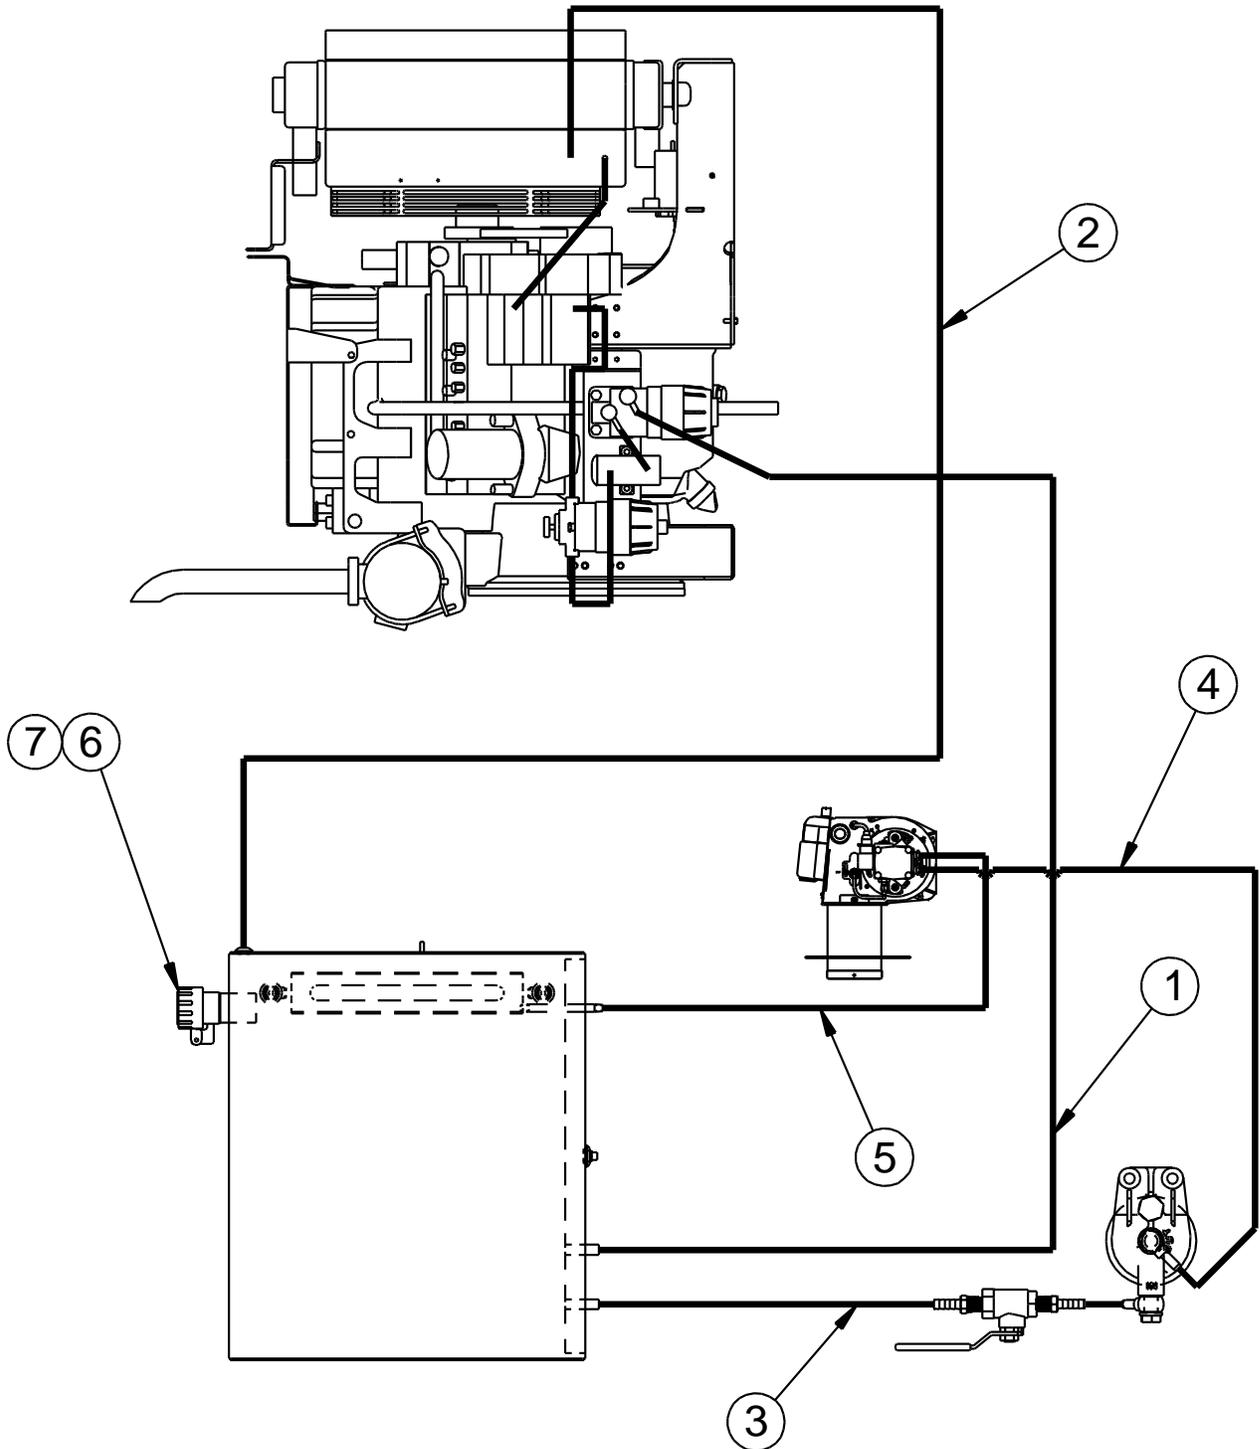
Esquema de la Tubería de Combustible Diésel – Motor 4LE2T
